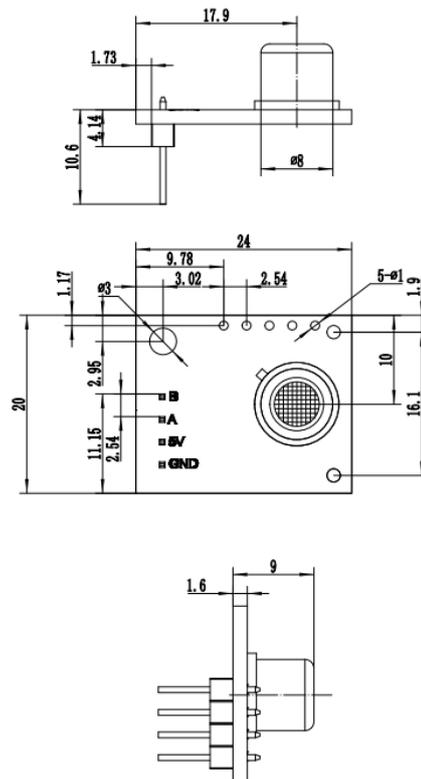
模组结构图 (模组尺寸公差±0.2mm)
